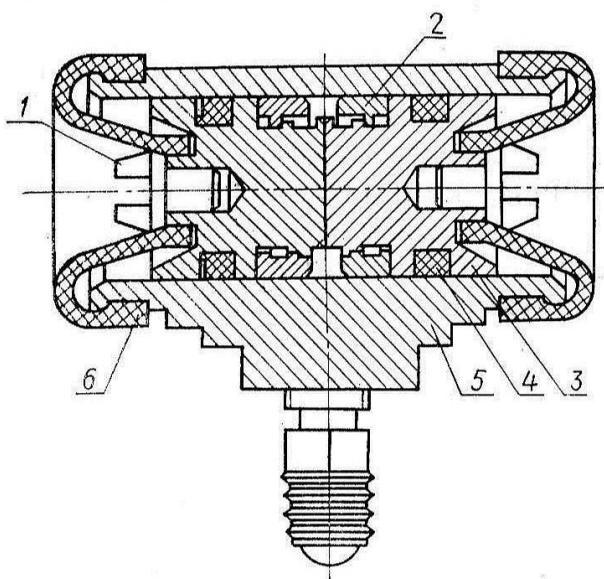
Колесный тормозной цилиндр с устройством для автоматического поддержания зазора между колодками и барабаном:
